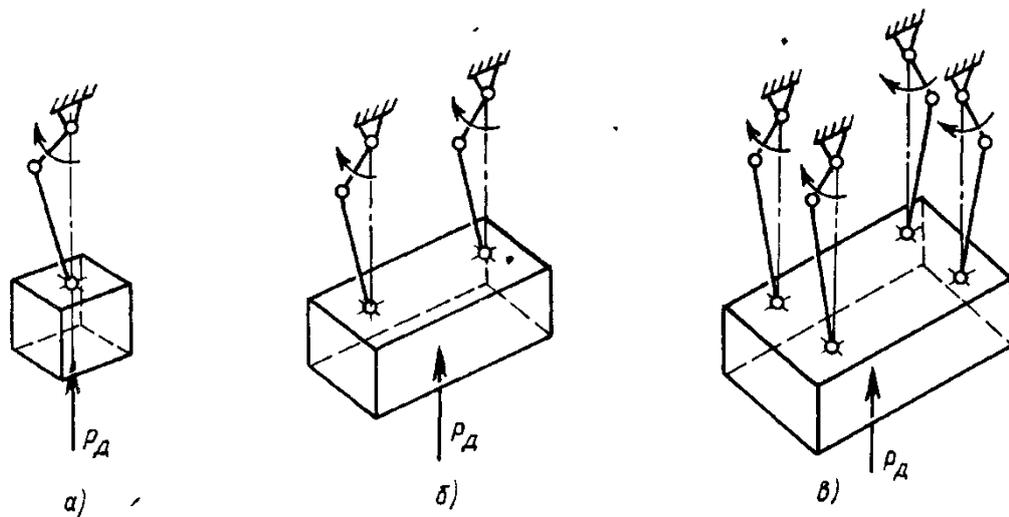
Схемы одно- (а), двух- (б) и четырехкривошипных (в) механизмов. Прессы механические для листовой штамповки.
